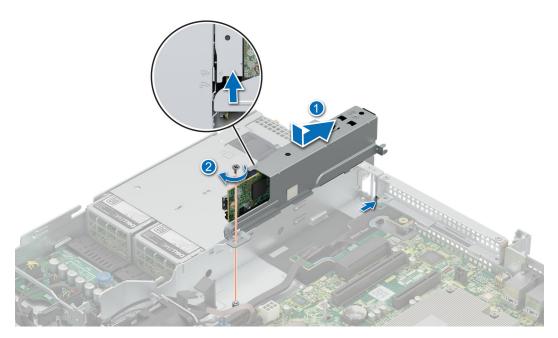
Installieren des BOSS-N1-Gehäuses
